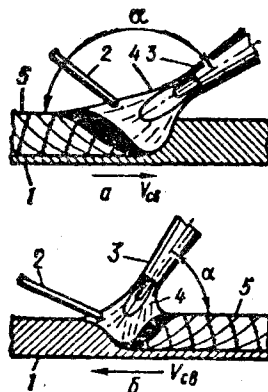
Схема газовой сварки: а — правым способом; б — левым
